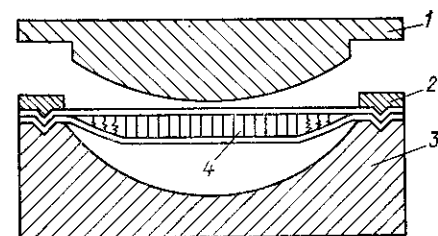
Приспособление для штамповки сотовых панелей:
